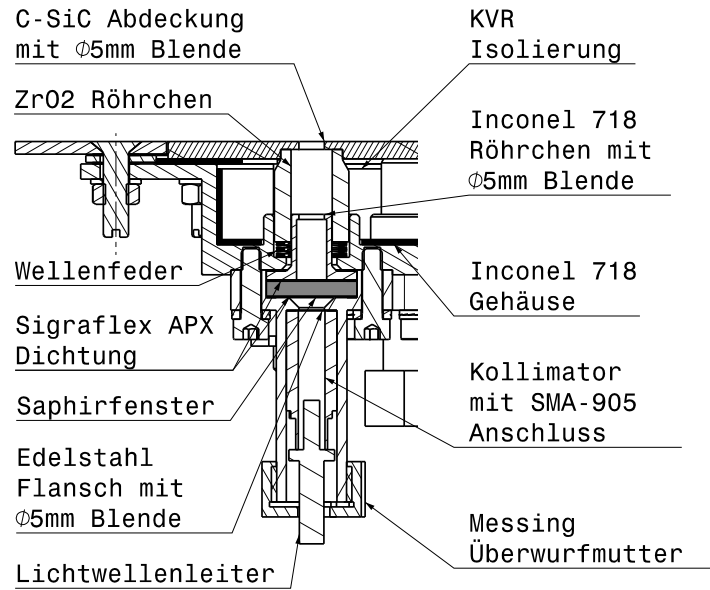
Schnittzeichnung Sensorkopf 2 [76]
